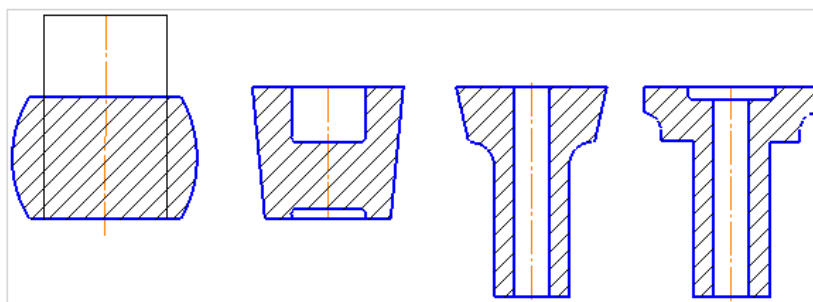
Четырехпереходная штамповка поковки с наметкой и прошивкой глухой полости
